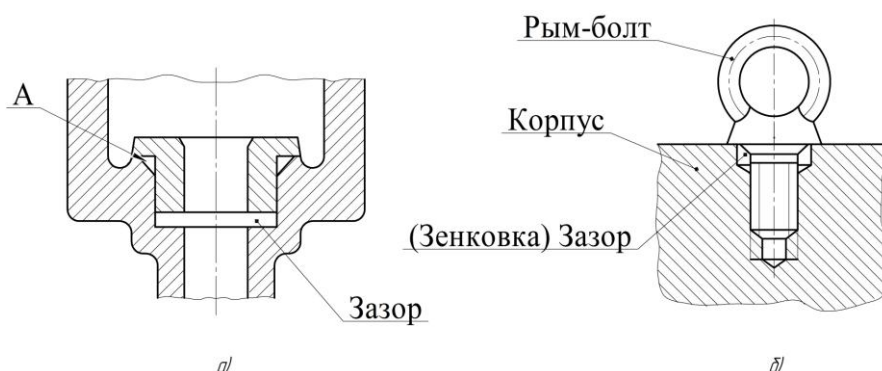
Технологические зазор и зенковка для плотного крепления деталей
